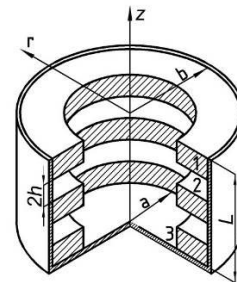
Модель цилиндрической заготовки с регулярными дискообразными щелями 2 , находящимися между слоями каркаса 1 ; 3 - условная оправка, определяющая направление течения газа
